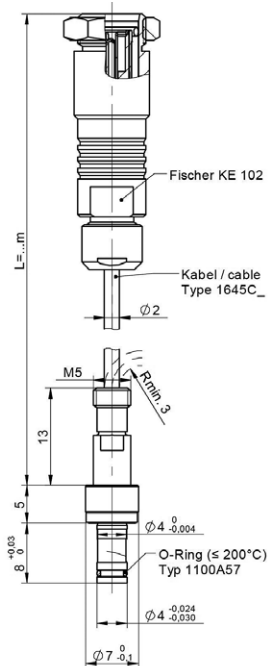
Drucksensor Typ 6177B mit Koaxial Kabel
